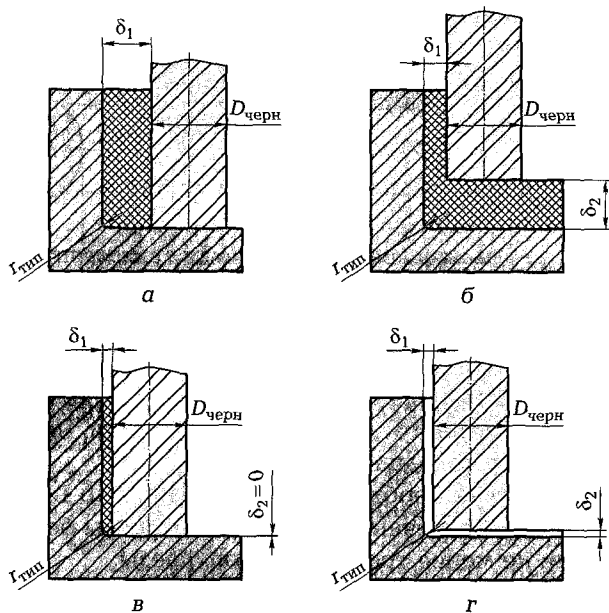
Расчет радиуса заточки фрезы гчерн для проведения черновой обработки:
